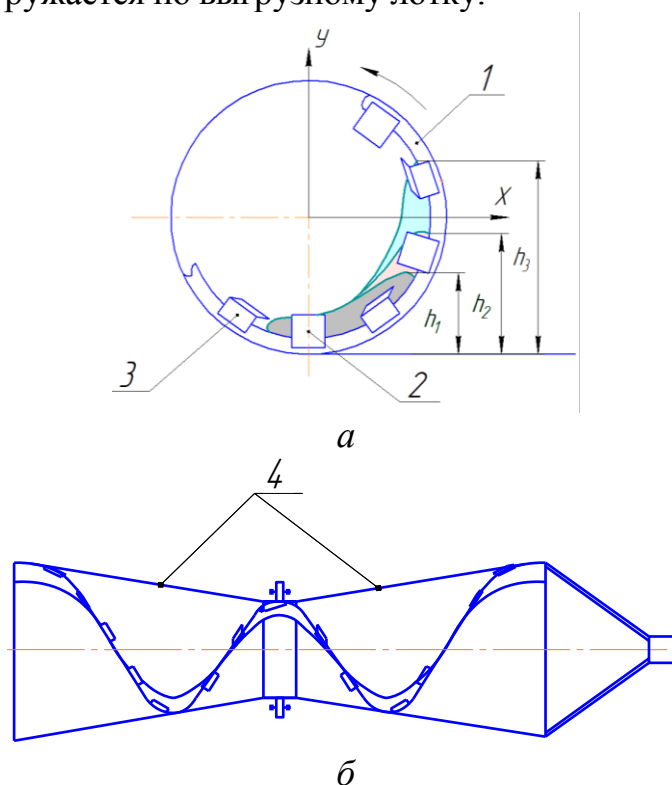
Конструктивно-технологическая схема нового смесителя кормов непрерывного действия: *а* – поперечный разрез; *б* – продольный разрез; 1 – шнековая навивка; 2 – удлинитель участка навивки; 3 - Г-образная лопатка; 4 – конусы бункера; h_1 , h_2 , h_3 – высота подъёма смеси шнековой навивкой, удлинителем и Г-образной лопаткой, соответственно.
